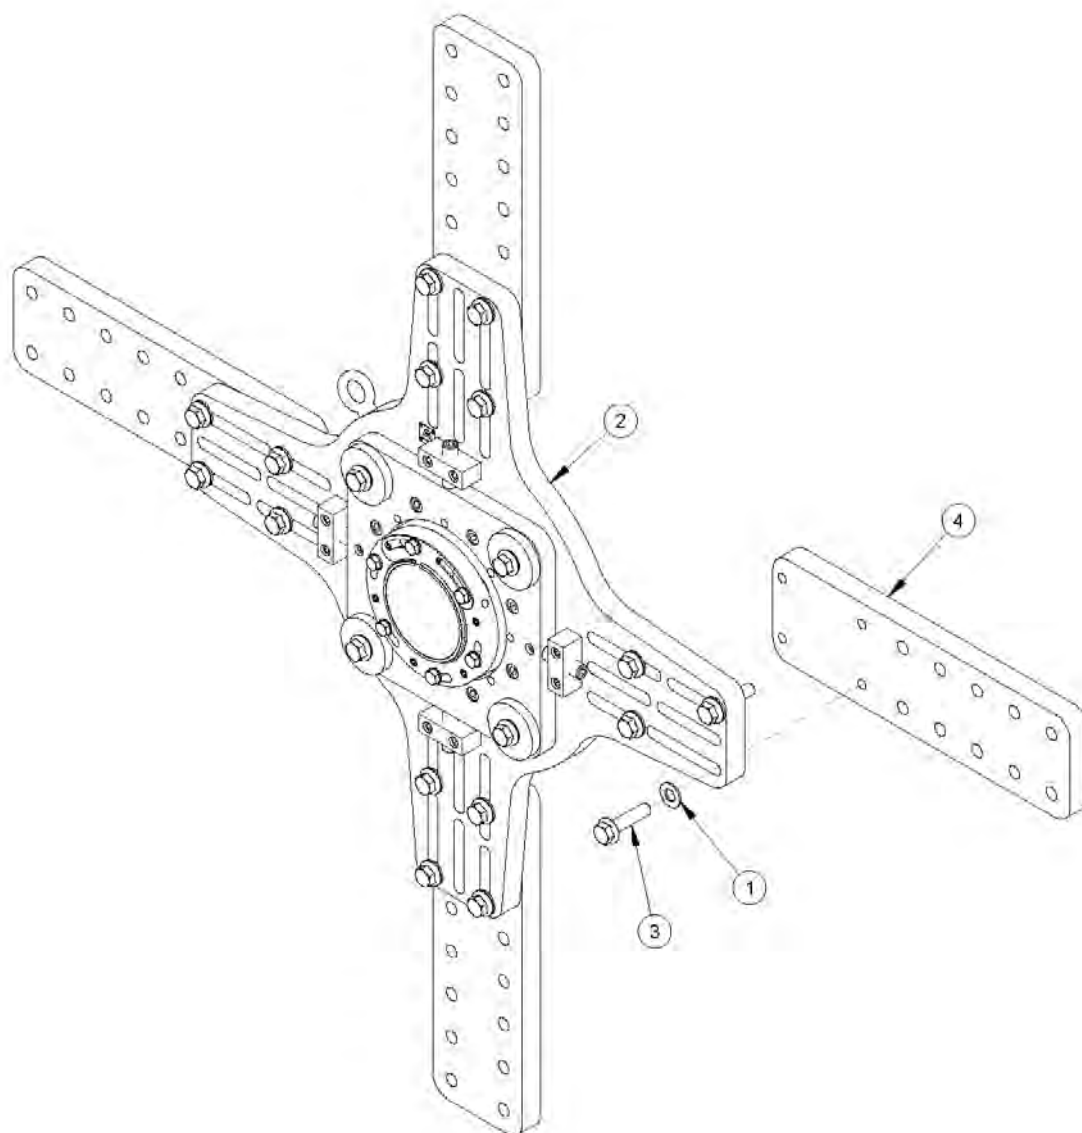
Блок осевой подачи в сборе, перечень деталей (кат. № 42407)
